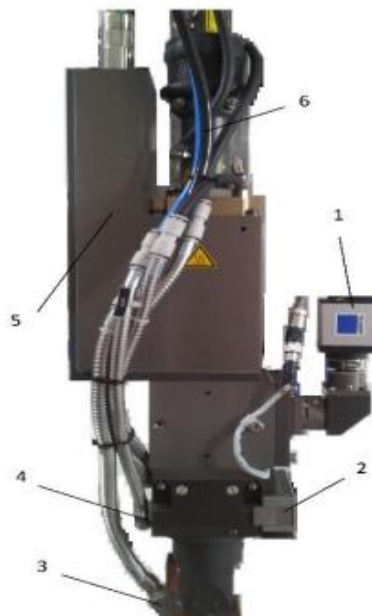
Cabeça de soldadura (1-câmara de monitorização; 2-vidro de proteção; 3-gás; 4-proteção adicional; 5-lente de foco; 6-refrigeração) [38]
